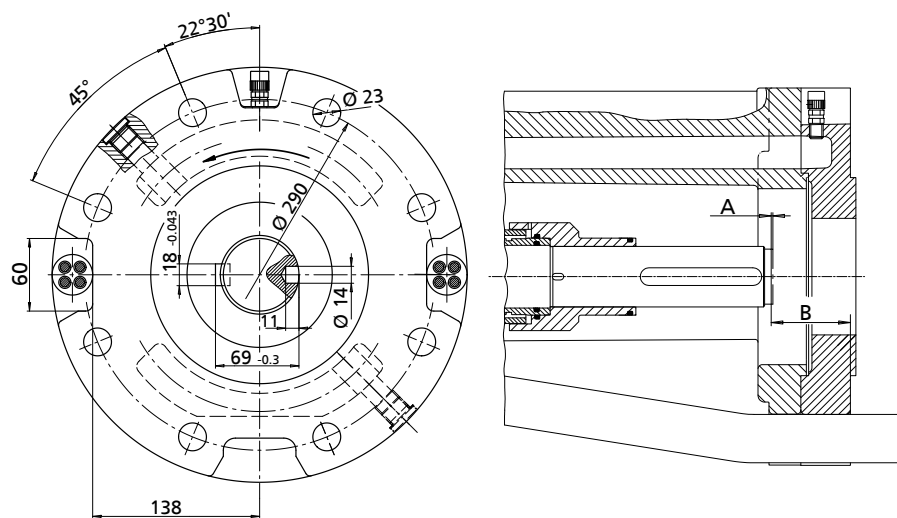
Присоединительный размер 14D, данные размера [мм]
